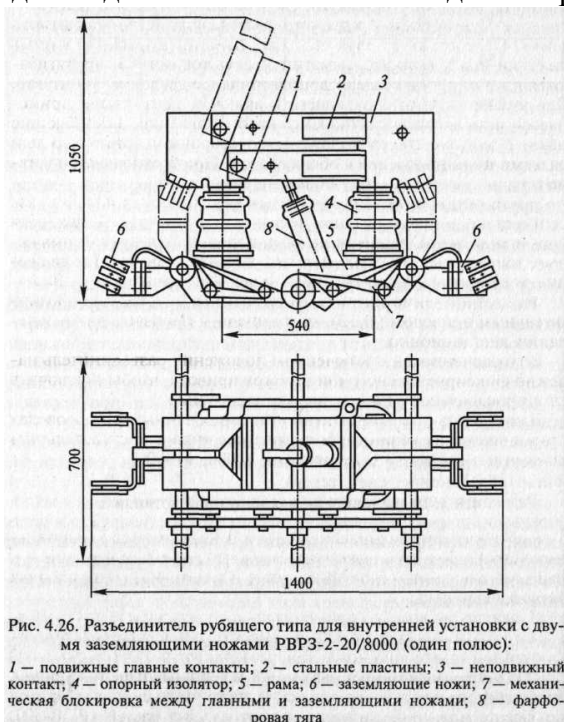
Разъединитель рубящего типа для внутренней установки с двумя заземляющими ножами РВРЗ-2-20/8000 (один полюс):
